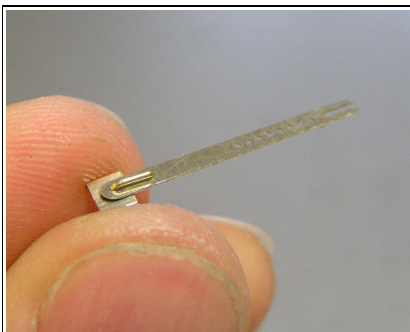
Den Lenkhebel auf die Halterung stecken, den Messingdraht kürzen und wie im Bild umbiegen.
